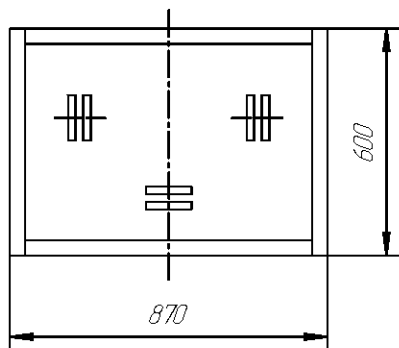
Габаритные, установочные, присоединительные размеры шкафов
